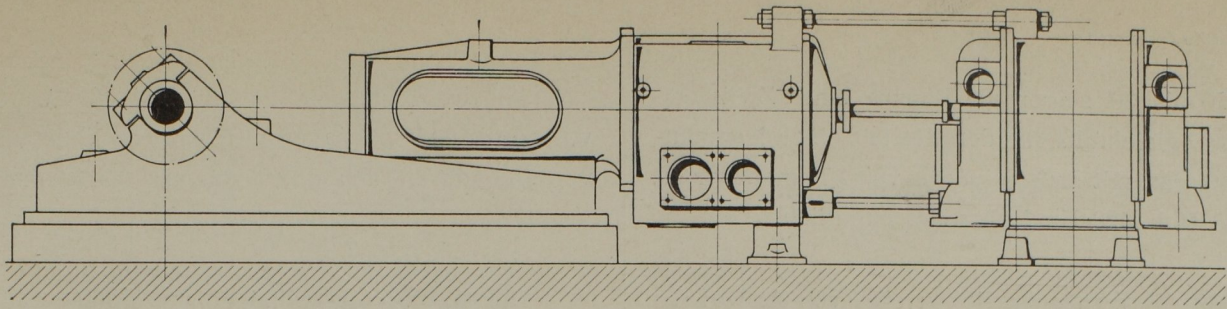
Seitenansicht des Kompressors. Masst. 1:30.
